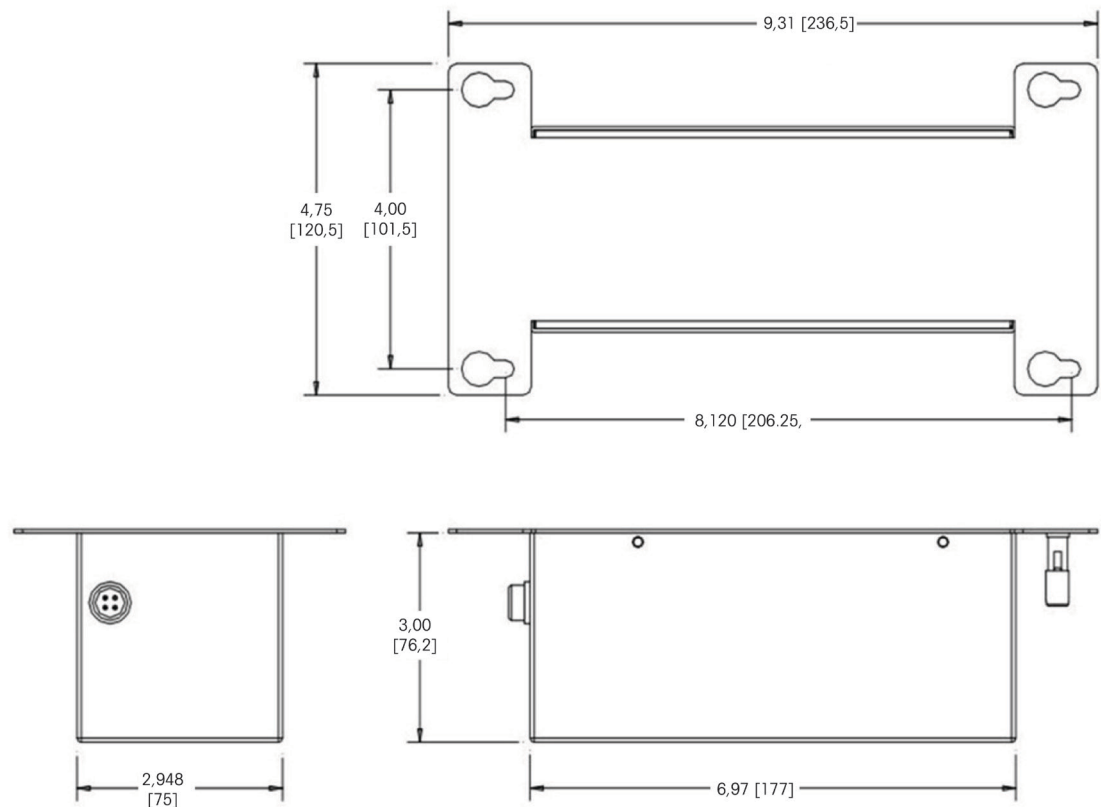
Dimensões gerais do pacote de baterias 64060625
